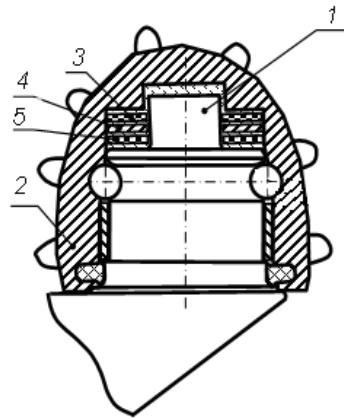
Компоновка комплексного упорного подшипника: 1 – цапфа; 2 – шарошка; 3 – верхняя шайба из металлофторопласта; 4 – стальная шайба; 5 – нижняя шайба из металлофторопласта
